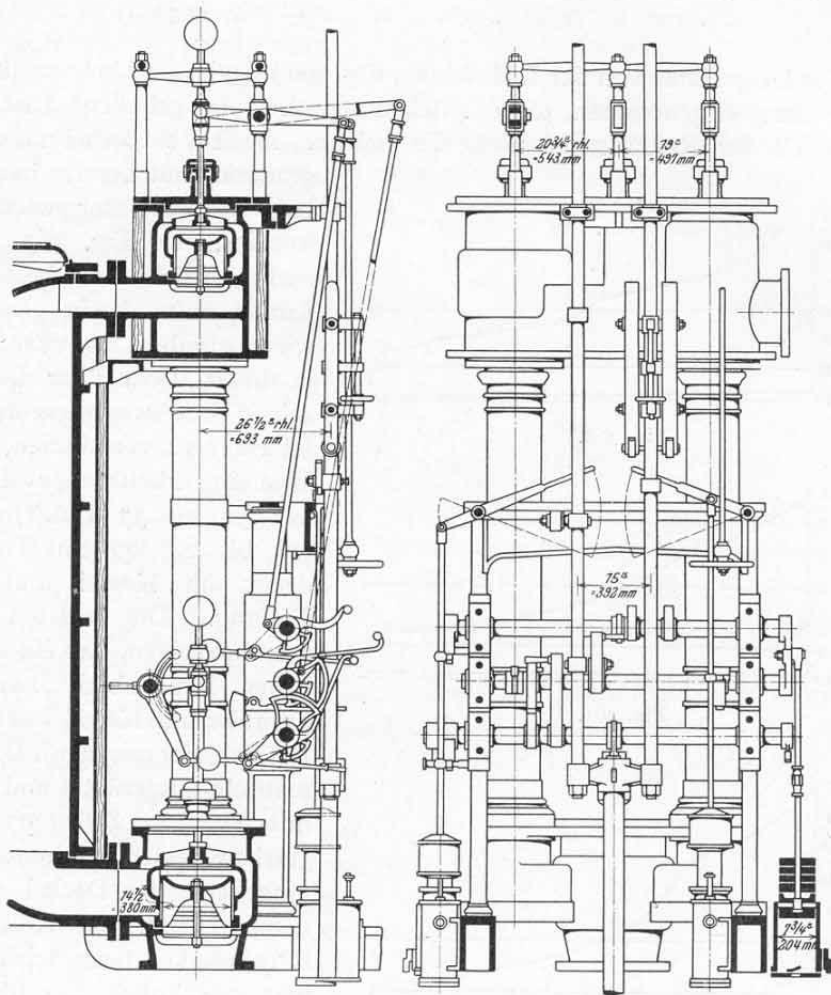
u. 359. Steuerung zur Maschine Fig. 357.
